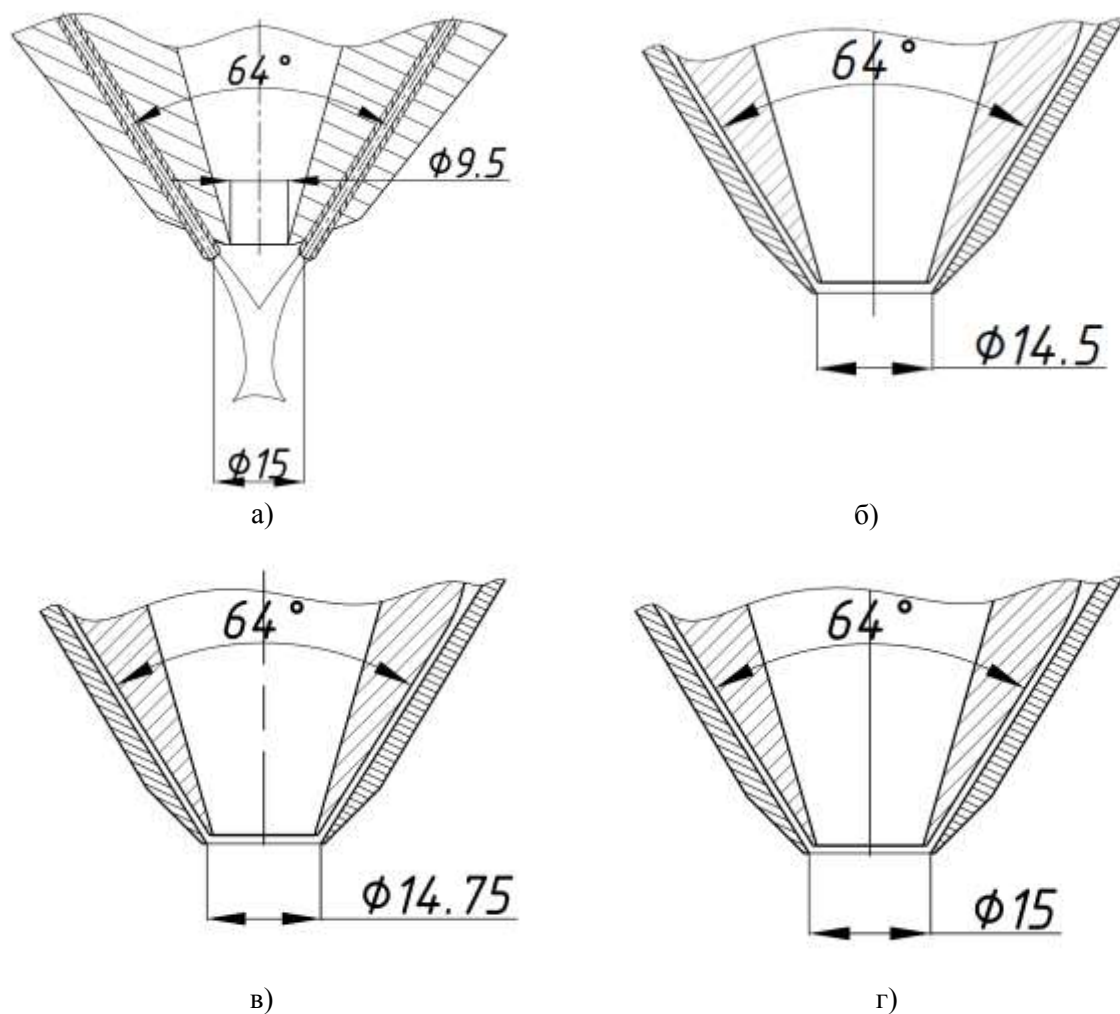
Эскизы рабочей части сопла с различными насадками для: четырехструйной подачи порошка (а) и коаксиальной подачи порошка (б - S 0,5; в - S 0,75; г - S 1,0)
